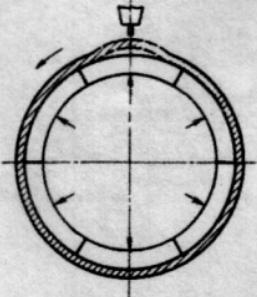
Схема подъема кронок при сварке кольцевого стыка на раздвижной оправке
